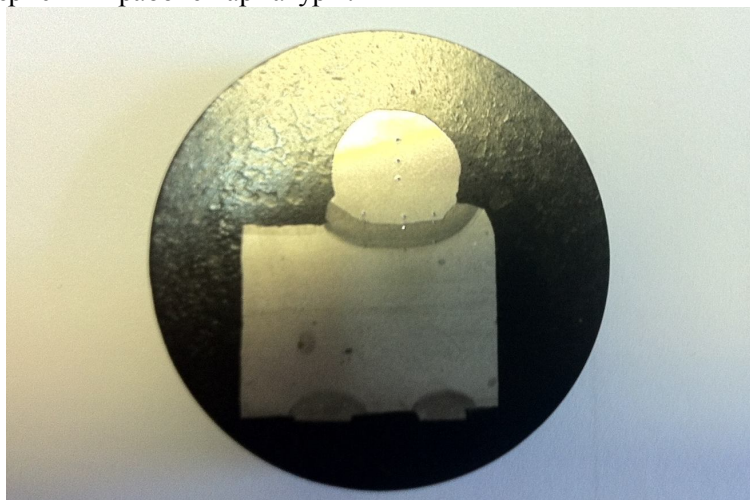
Микрошлиф сварного соединения, запрессованный в компаунд
